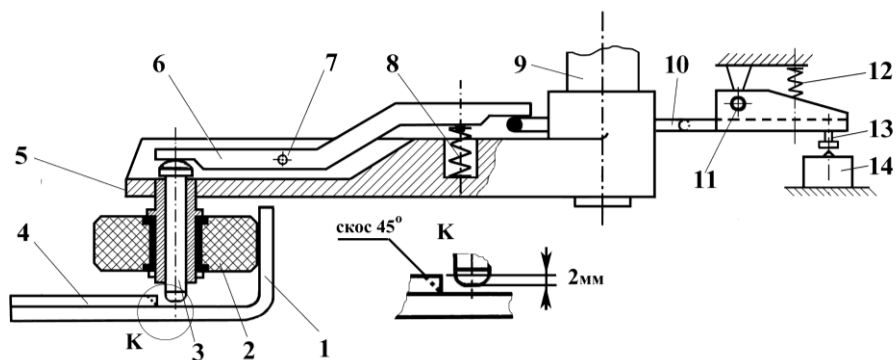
Схема конструкции привода контакта реверса движения створок:
